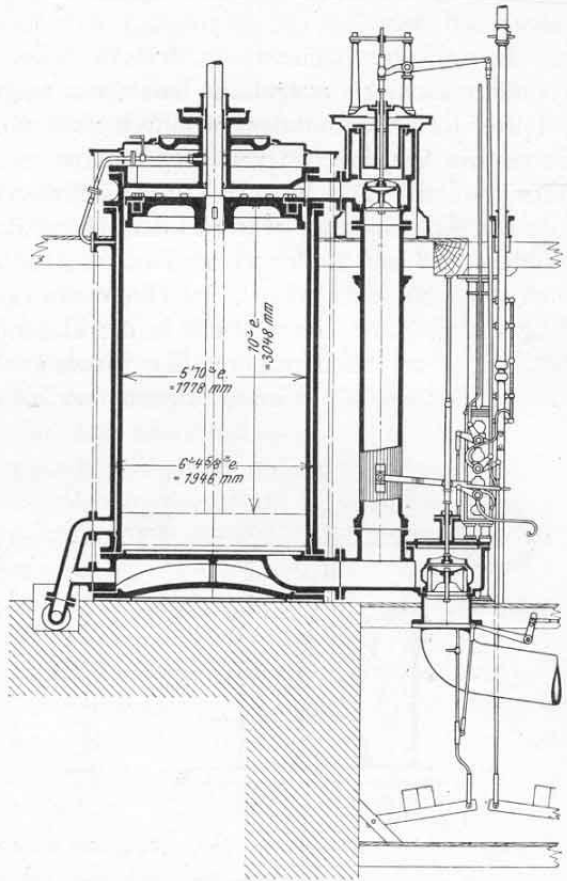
Zylinder und Steuerung zur Maschine Fig. 323.
